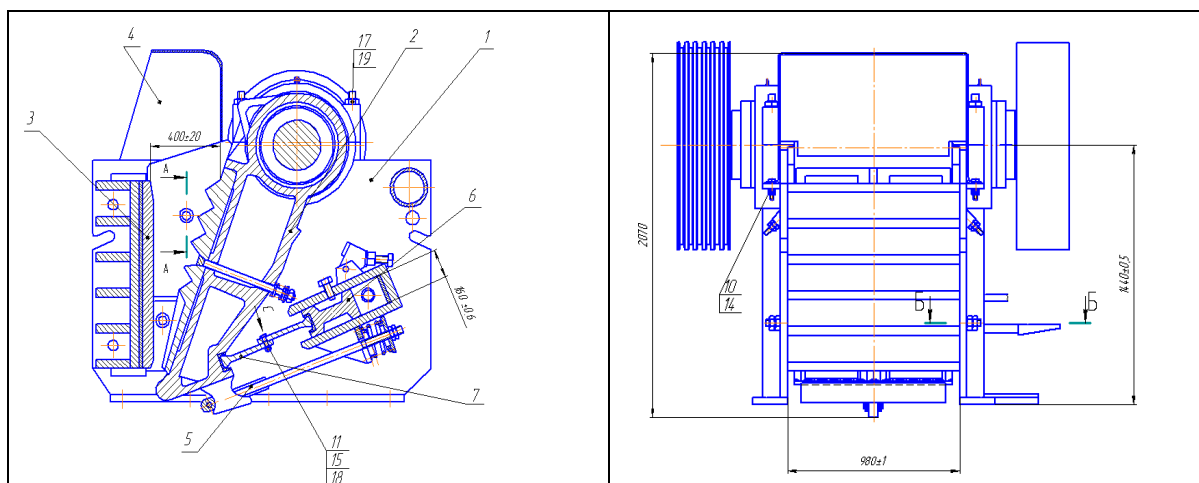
Общий вид щековой дробилки 1-станина; 2- неподвижная дробящая плита; 3,15- упоры; 4,14- боковые футеровки; 5- подвижная дробящая плита; 6- шток; 7- эксцентриковый вал; 8-подвижная плита; 9- шток; 10- механизм регулирования выходной щели; 11 – тяга; 12 – распорная плита; 13- сменный сухарь; 16- откидной упор; 17 – винт; 18- привод механизма регулирования выходной щели
